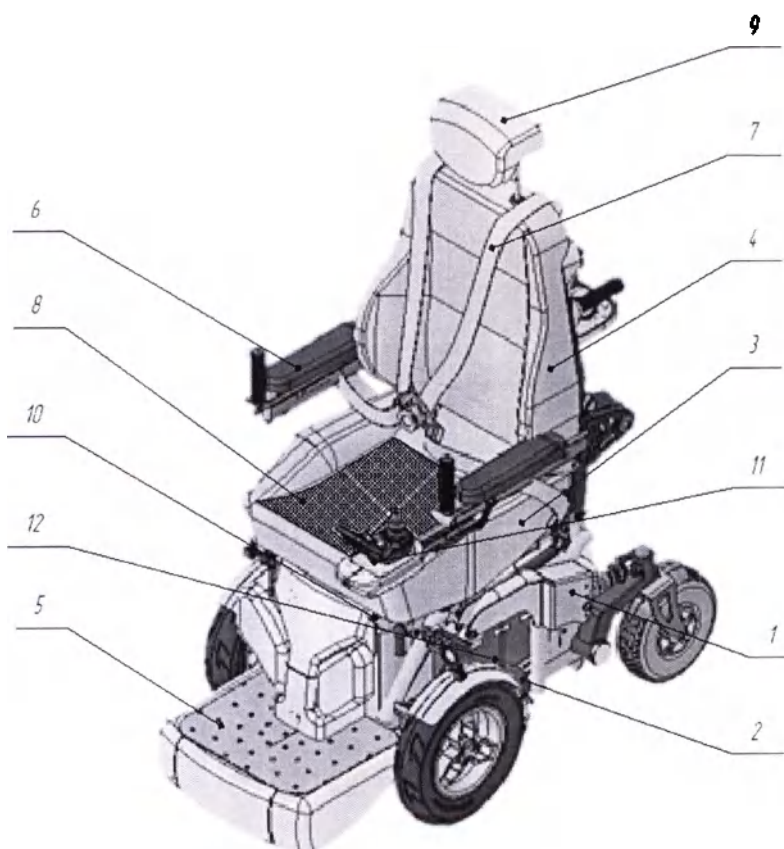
Внешний вид кресла-коляски «Гефест С»
